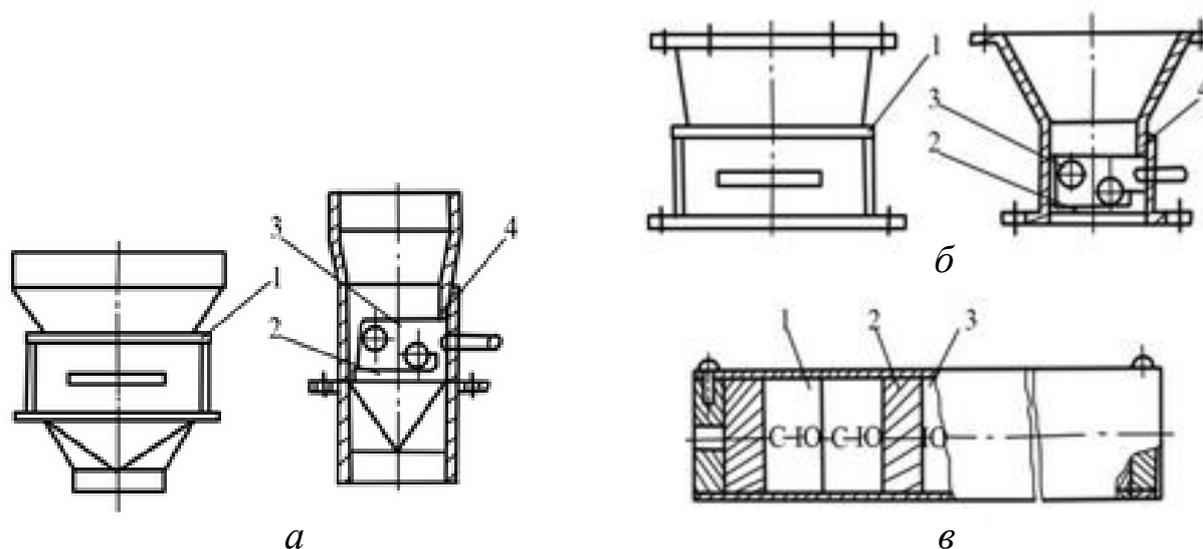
Магнитный сепаратор: а – У1-БМЗ; б – У1-БМЗ-01; 1 – корпус; 2 – направляющие; 3 – блок магнитов; 4 – заслонка; в – цилиндрический магнит: 1 – дисковые магниты; 2 – вставка; 3 – кожух
